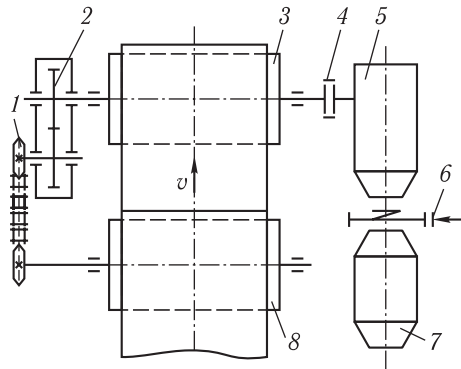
Схема приводу крутопохилого конвеєра з притисною стрічкою: 1 — ланцюгова передача; 2 і 5 — редуктори; 3 і 8 — привідні барабани; 4 — муфта; 6 — гальмо; 7 — електродвигун
